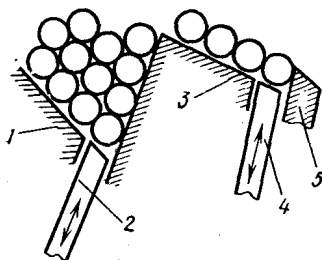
Схема бункерного устройства с захватным механизмом
